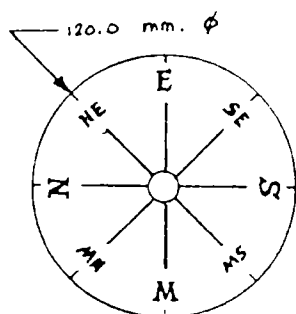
Sur du carton blanc dessiner le cadran et découper-le. Coller le sur le support.
